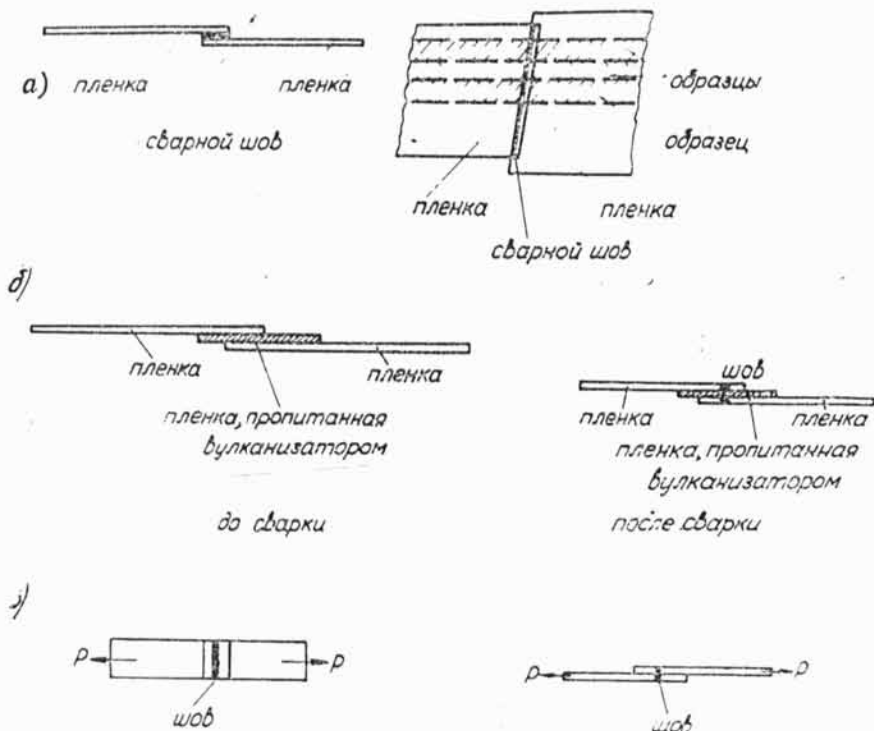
Схема сварки облученного полиэтилена.
